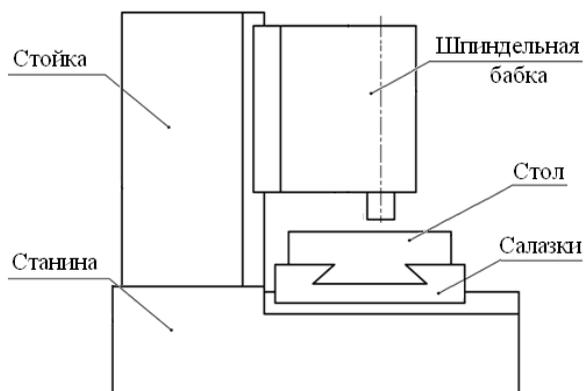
Типовые базовые детали и упрощенная компоновка вертикального бесконсольно-фрезерного станка
